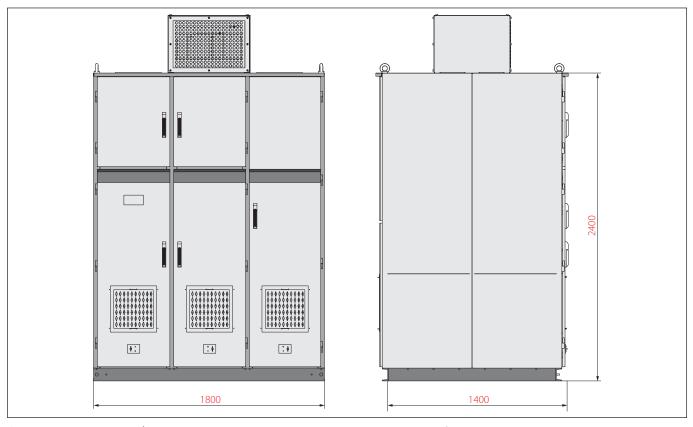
Корпус шкафа токоограничивающего реактора типоразмера ЕСО4
